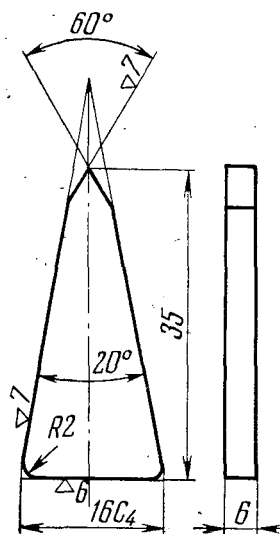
Ножи для накалывания к барабанам станка ПКБ ЦП МПС
